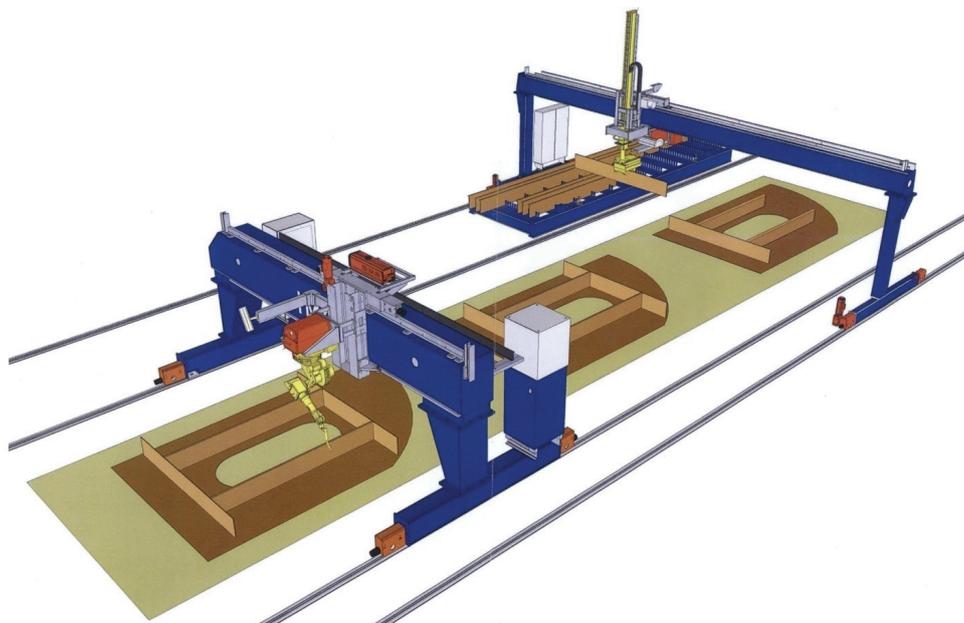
Линия механизированной сборки и роботизированной сварки микропанелей
